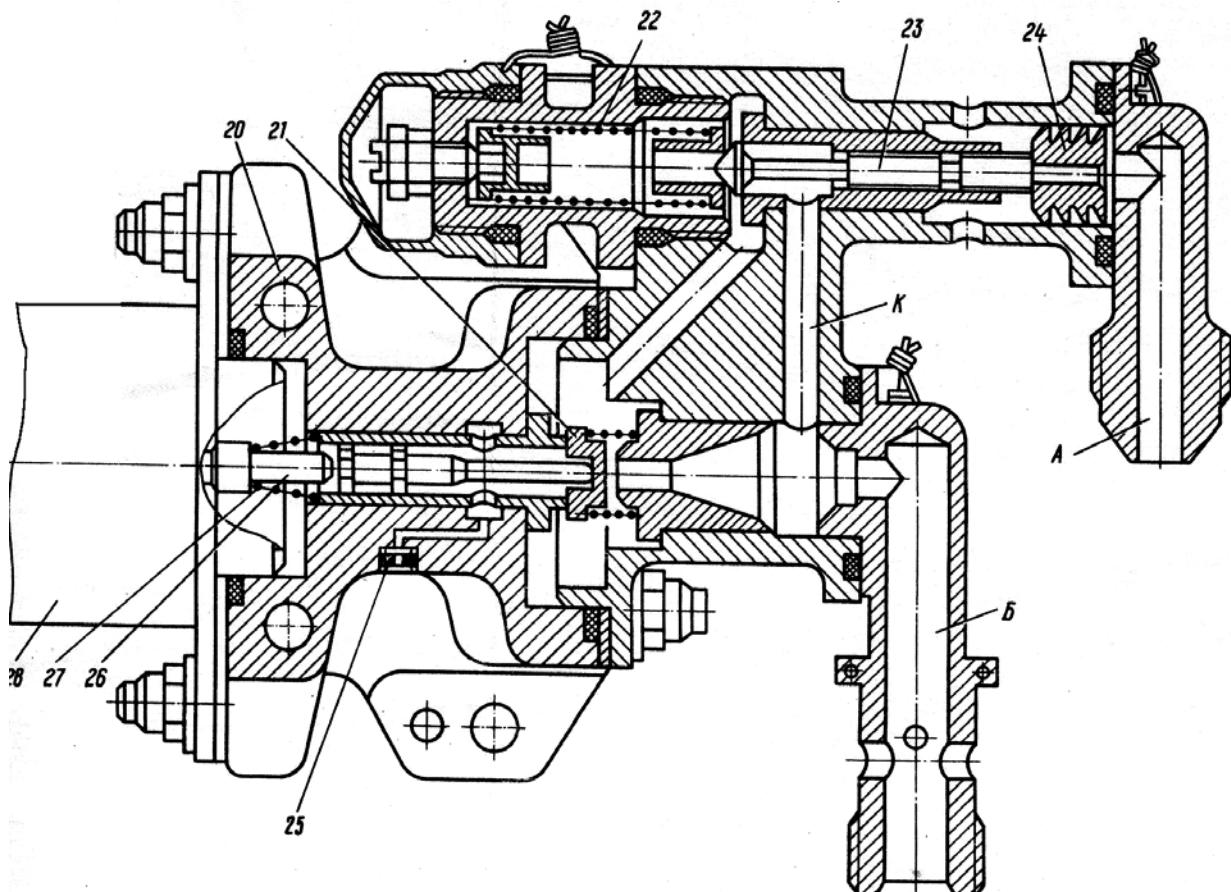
Командный агрегат воздушного стартёра СВ-78БА
